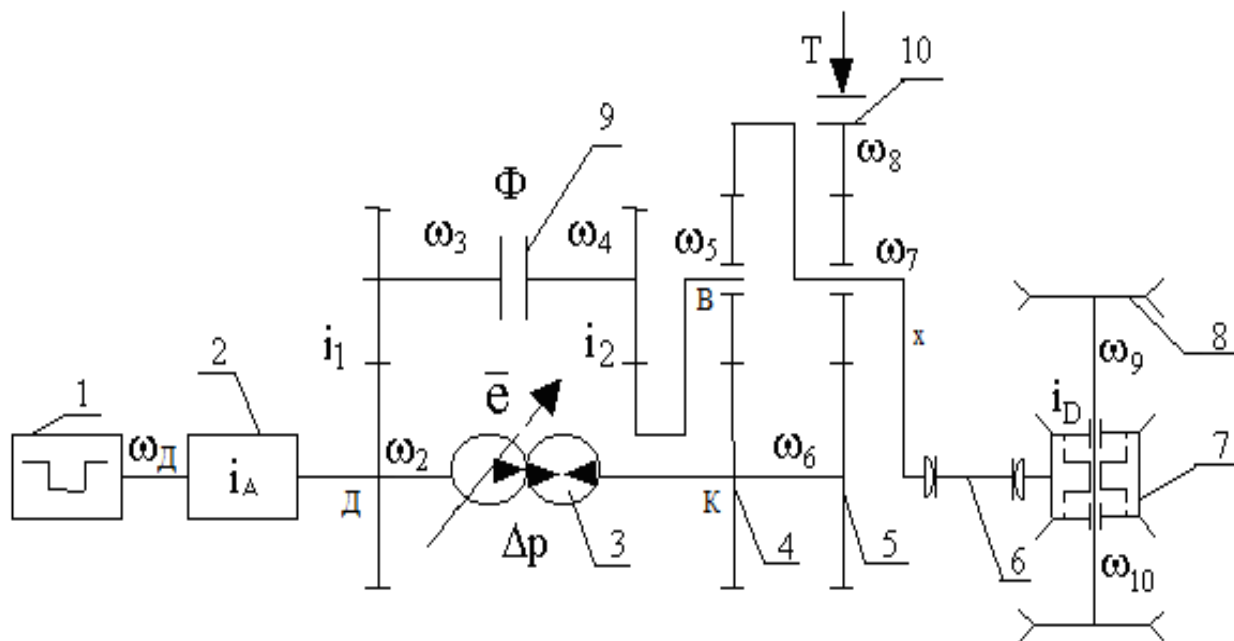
ГОМТ с планетарным механизмом на выходе и угловые скорости ее звеньев: 1 – ДВС; 2, 7 – редукторы; 3 – ГОП; 4, 5 – зубчатые передачи; 6 – вал; 8 – колесная пара; 9 – фрикцион; 10 – тормоз
